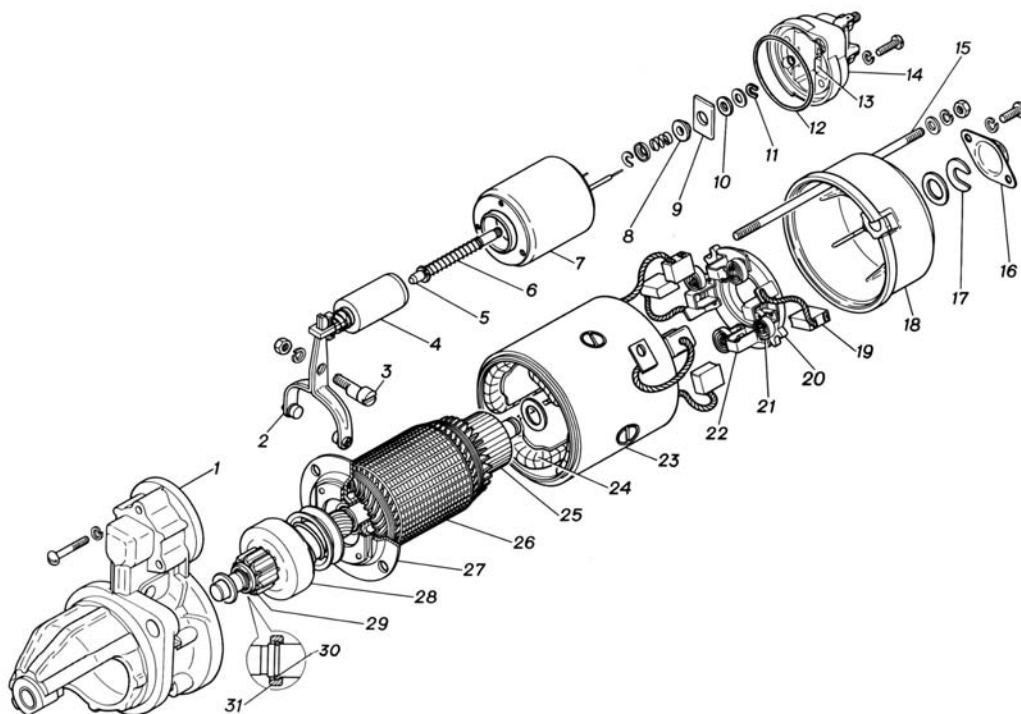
Стартер 42.3708-10: 1 - крышка со стороны привода; 2 - рычаг; 3 - ось рычага; 4 - сердечник тягового реле; 5 - шток тягового реле; 6 - возвратная пружина; 7 - тяговое реле; 8 и 10 - изоляционные втулки; 9 - контактная пластина; 11 и 17 - запорные шайбы; 12 - уплотнительное кольцо; 13 - контактный болт; 14 - крышка тягового реле; 15 - стяжная шпилька; 16 - защитный колпак; 18 - крышка со стороны коллектора; 19 - щетка; 20 - держатель щеток; 21 - пружина щетки; 22 - щеткодержатель; 23 - корпус; 24 - обмотка возбуждения; 25 - коллектор; 26 - якорь; 27 - промежуточная опора; 28 - привод с роликовой муфтой свободного хода; 29 - шестерня; 30 - пружинное кольцо; 31 - упорная втулка
